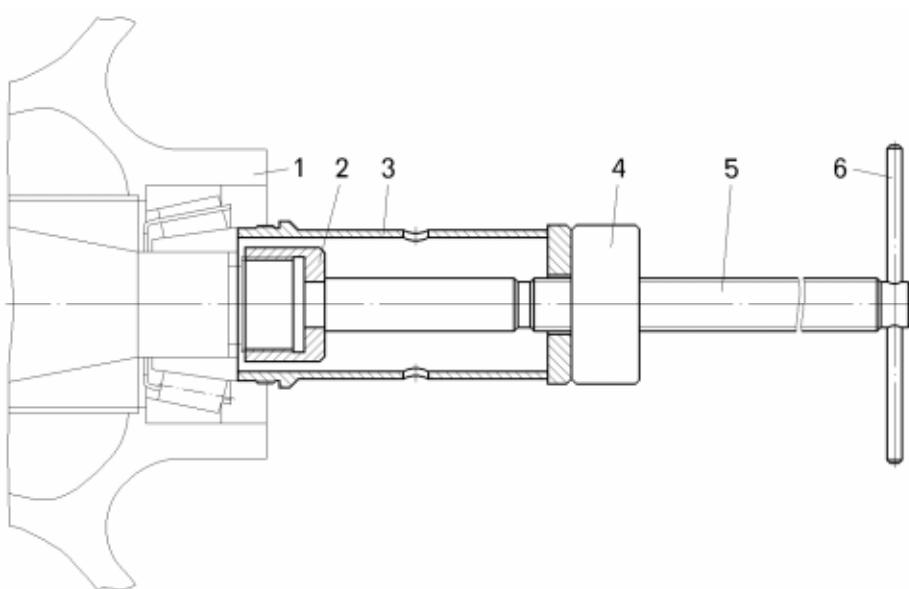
Приспособление для запрессовки ступицы переднего колеса:
